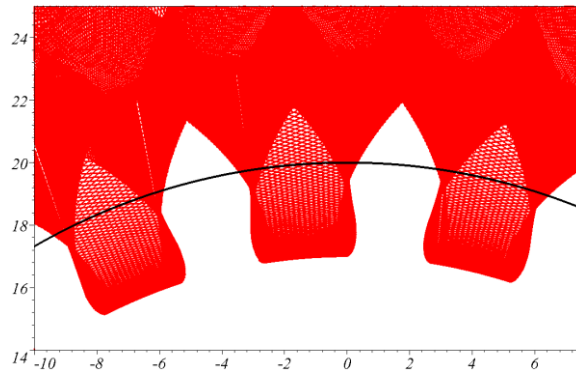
Форми профілів зубів нерухомого зубчатого колеса для планетарного механізму
